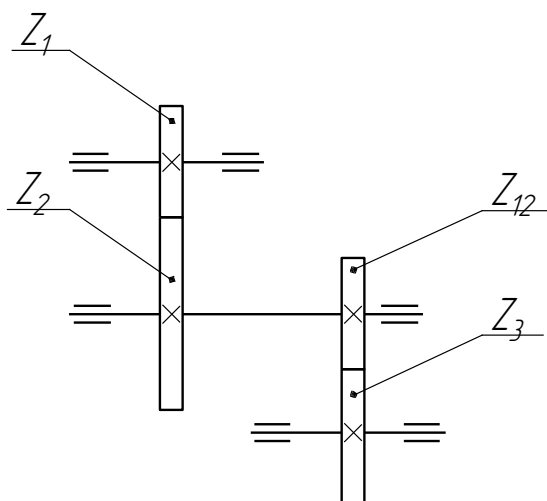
Кинематическая схема двухступенчатого редуктора
